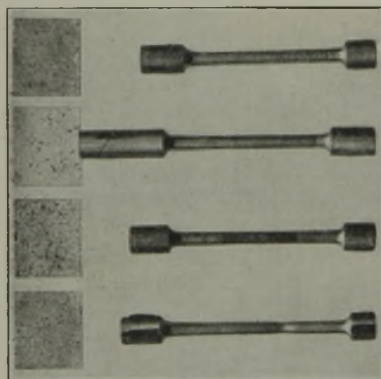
Einfluß einer Nachbehandlung der Schweiße auf ihre Festigkeitseigenschaften. (Elektrische Schweißung; Flußstahl; Zerreißstäbe nur aus Schweiße bestehend.)
